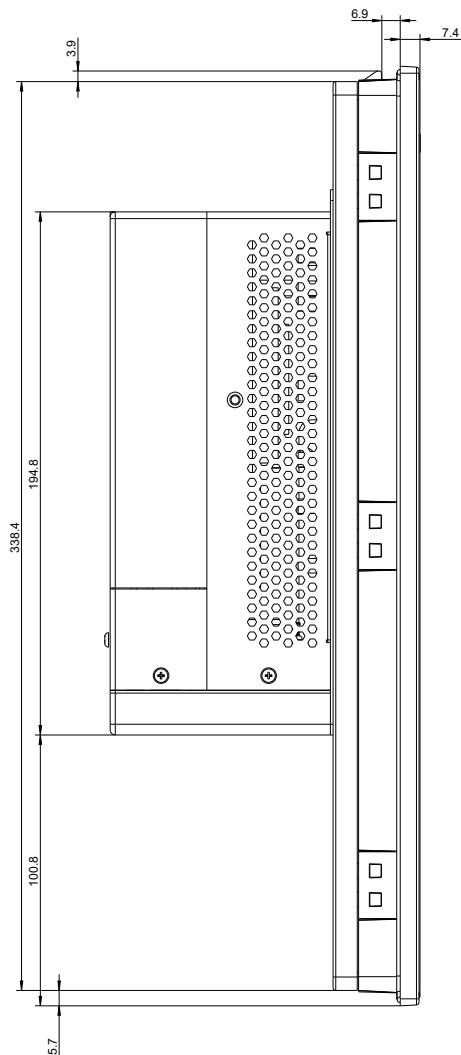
Размеры корпуса устройства VR4x21, вид слева
